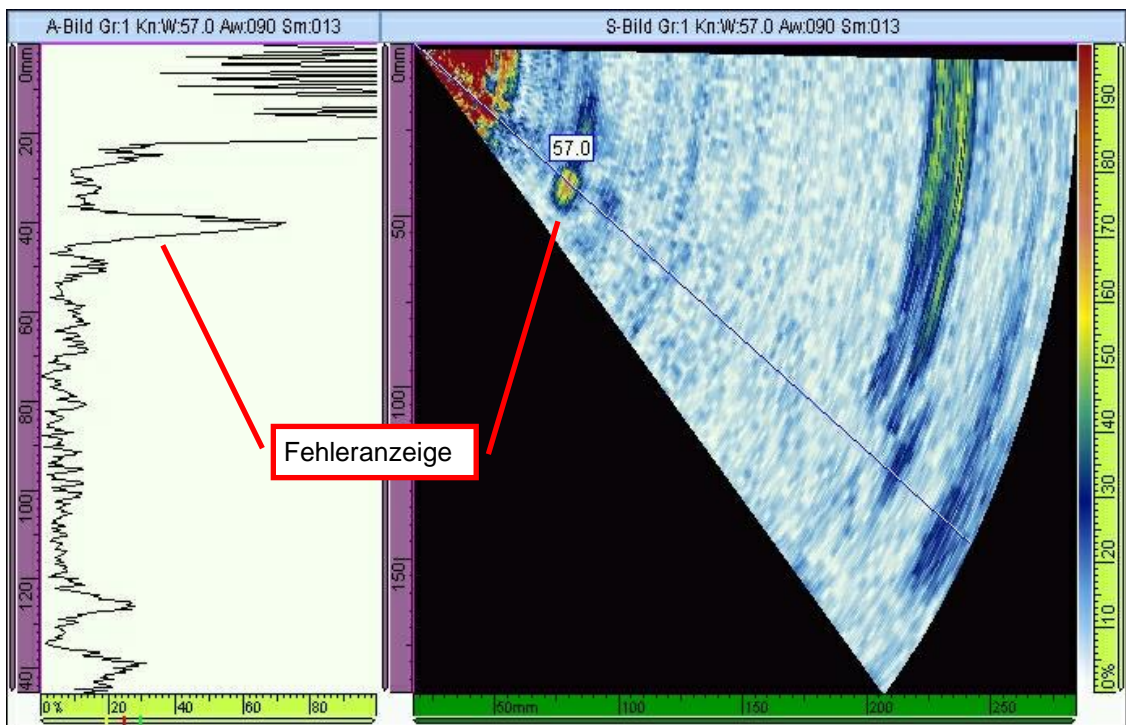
Ultraschall-A-Bild und Sektorscan: 2 mm Testfehler rückseitig vor der Schweißnaht
